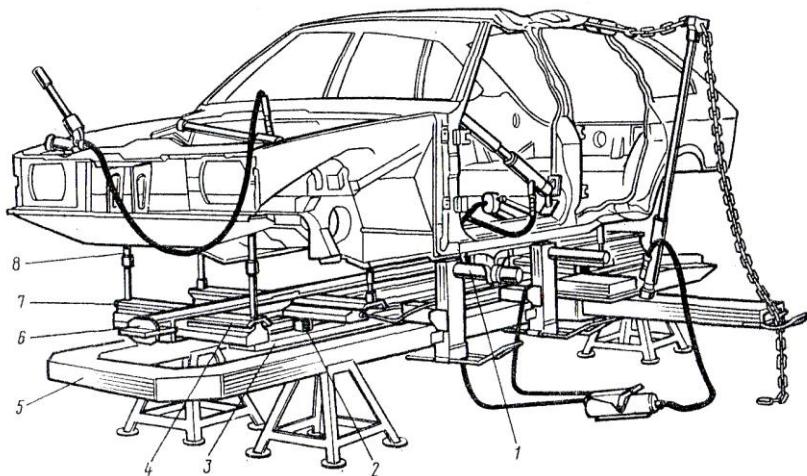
Измерительная платформа «Блэкхок Р-188», установленная на стенд для правки (многоцелевой), и закрепленный кузов:
